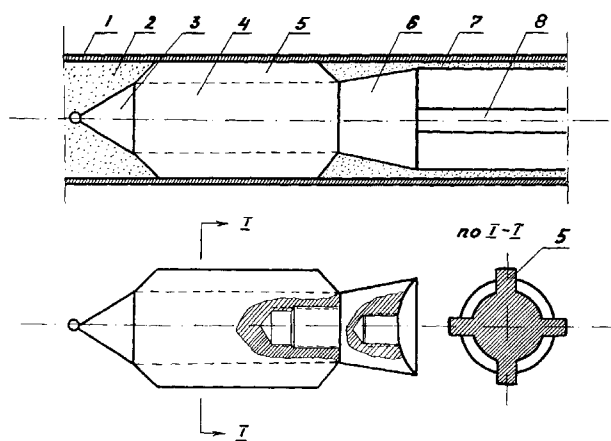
Схема пристосування для нанесення каталізатора на внутрішню поверхню труб
